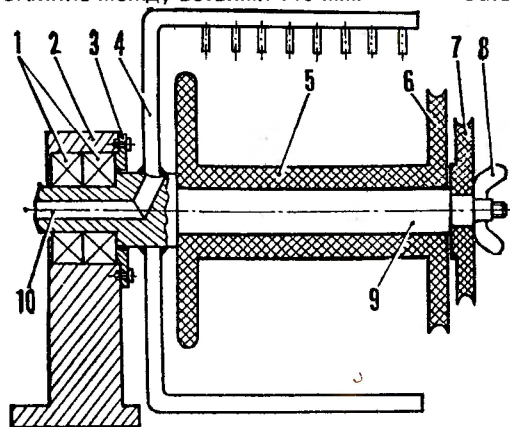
Веретено прялки: 1 — подшипники вала, 2 — стойка, 3 — крышка подшипников, 4 — рогулька, 5 — шпулька-катушка, 6 — шкив-щечка катушки, 7 — шкив вала, 8 — гайка, 9 — вал, 10 — коленчатый канал.
